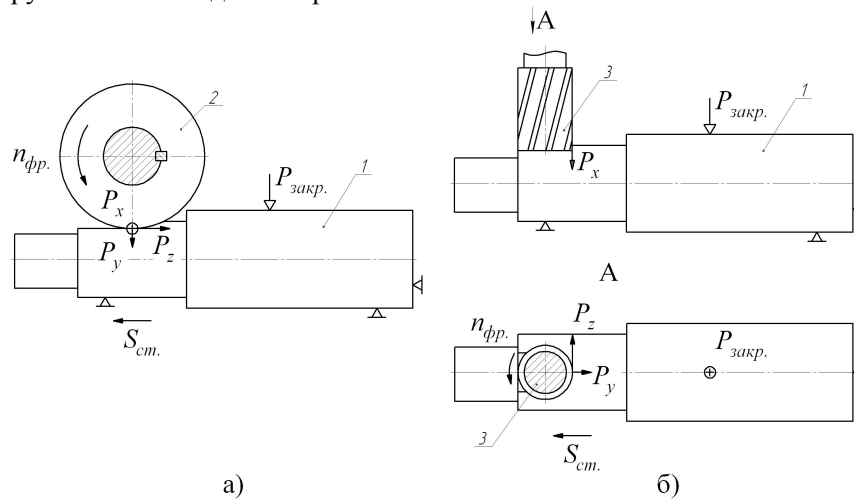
Схеми сил різання при фрезеруванні циліндричною фрезою (а) і кінцевою фрезою (б): 1 – ступінчастий вал; 2 – циліндрична фреза; 3 – кінцева фреза; P_x – осьова складова сили різання; P_y – радіальна складова сили різання; P_z – дотична складова сили різання; $P_{закр.}$ – сила закріплення; $n_{фр.}$ – частота обертання фрези, $S_{ст}$ – подача стола верстата
